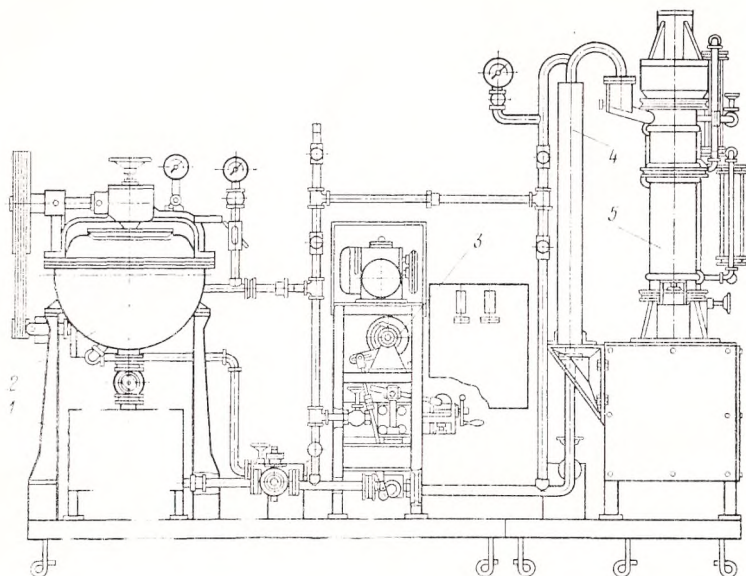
Установка для приготовления помады ШПА конструкции ВНИИКП: 1 — сборник для сиропа; 2 — открытый варочный котел с мешалкой; 3 — плунжерный насос; 4 — змеевиковый подогреватель; 5 — пленочный кристаллизатор
